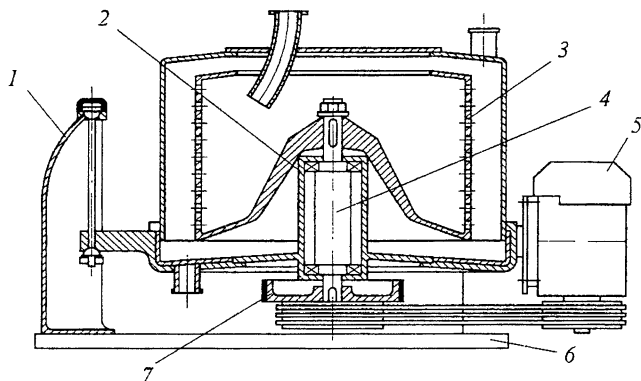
Конструктивная схема центрифуг типа ФМБ и ОМБ:
